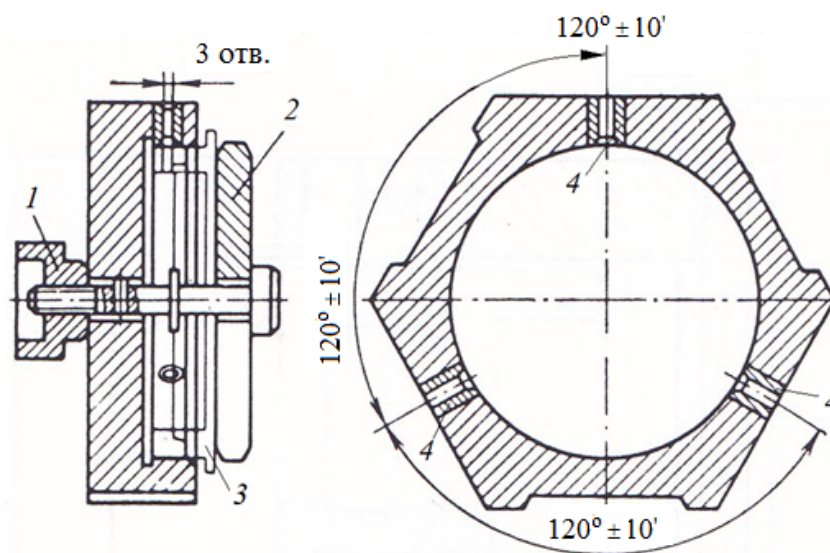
Пример кантующегося кондуктора для сверления отверстий на поверхности вращения:
